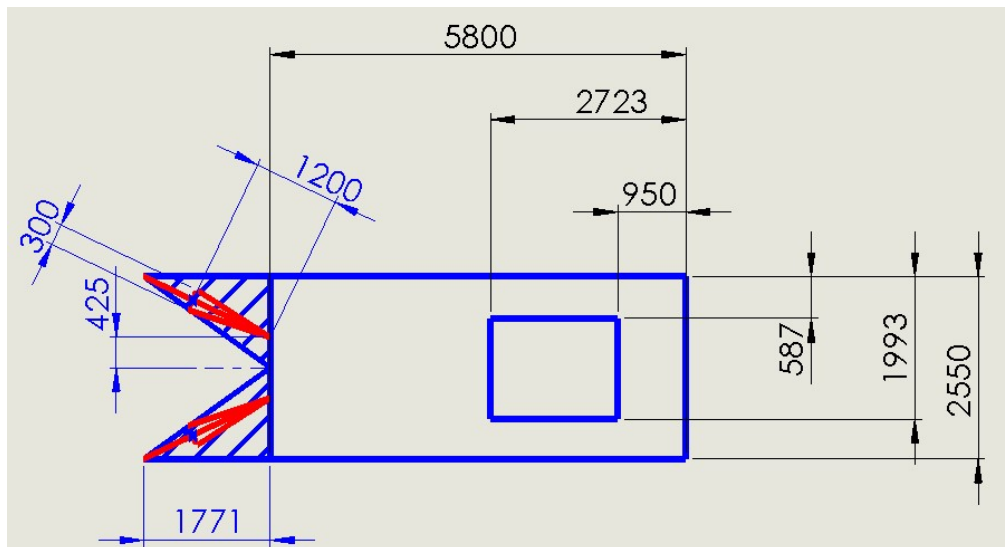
Vista Planta - Detección de sensores ultrasonidos
